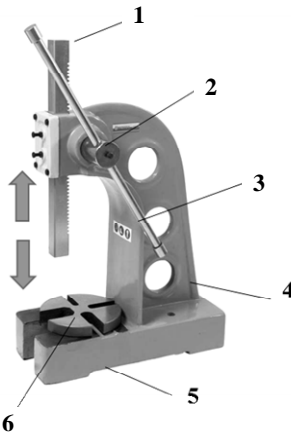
Приспособление для запрессовки и выпрессовки поршневого пальца:
